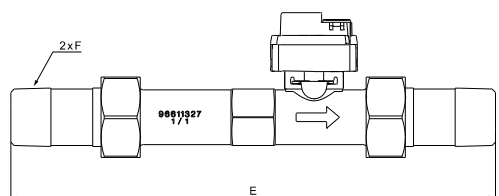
Размеры, VFS, 5-100 л/мин, с адаптерами
